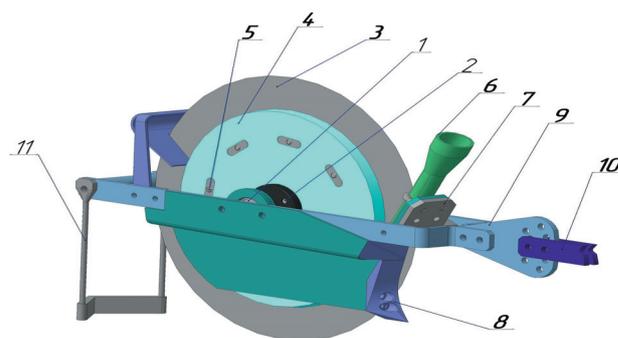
Общий вид комбинированного дискового сошника зерновой сеялки:
